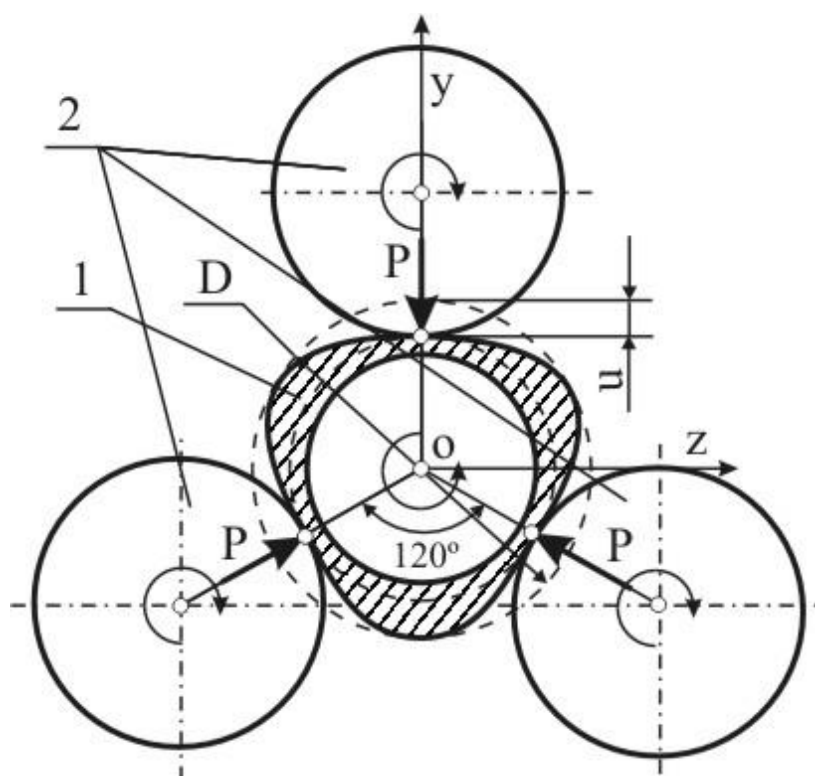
Схема релаксации остаточных напряжений коротких кольцевых деталей: 1 - деталь, 2 - вращающиеся валки
